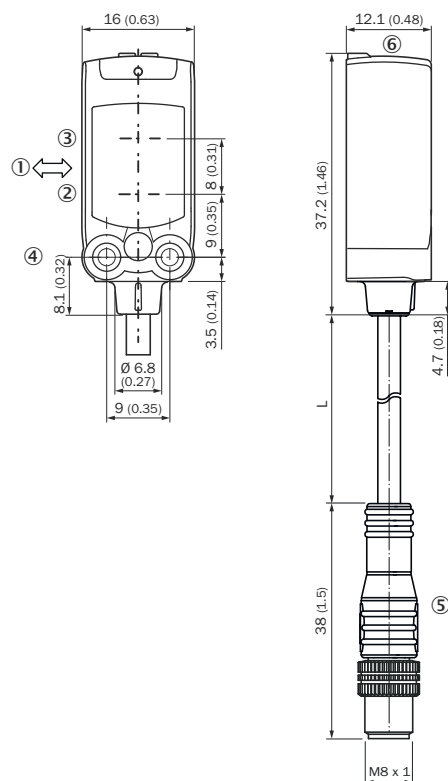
Масштабный чертёж, кабель со штекером M8, резьбовое соединение с накаткой
